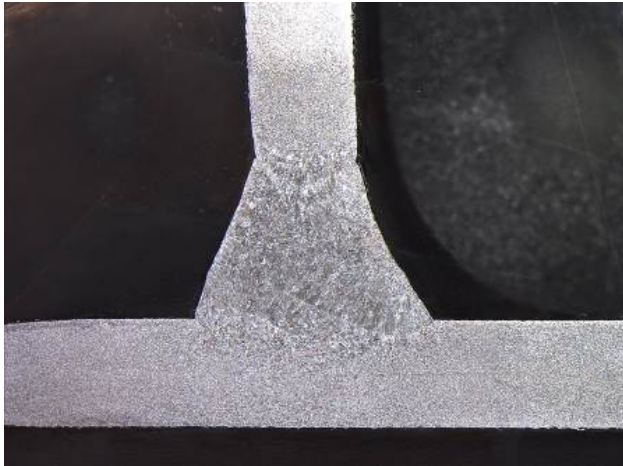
Der Schliff zeigt, wie sauber und wirtschaftlich der wärmereduzierte Fügeprozess abläuft – einseitig geschweißter T-Stoß an 4-Millimeter-Druckbehälterstahl
